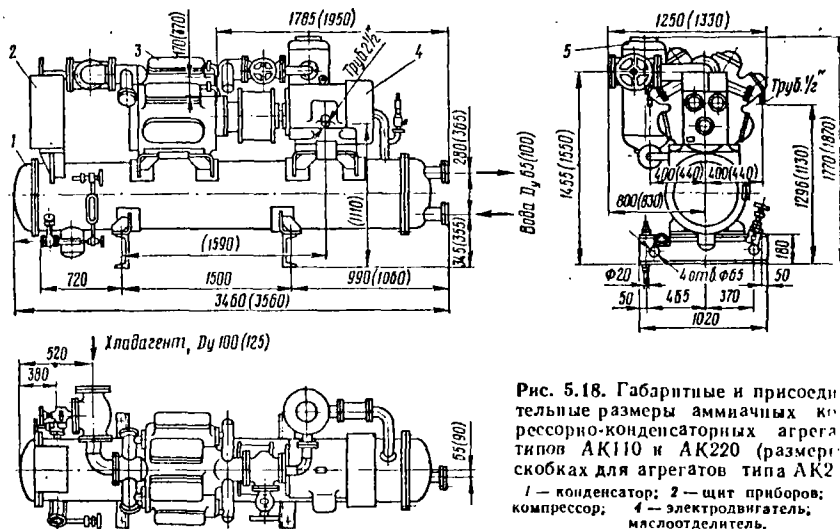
Габаритные и присоединительные размеры аммиачных компрессорно-конденсаторных агрегатов АК110 и АК220 (размеры скобок для агрегатов типа АК2): 1 — конденсатор; 2 — щит приборов; компрессор; 4 — электродвигатель; маслоотделитель.
